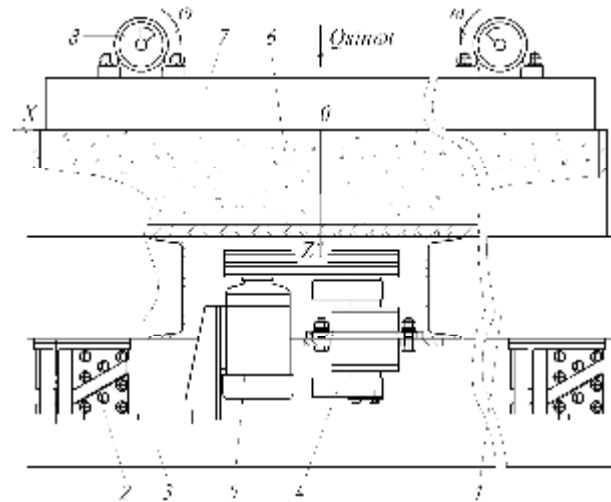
Схема вибрационной установки с пригрузом для формирования бетонных и железобетонных изделий
